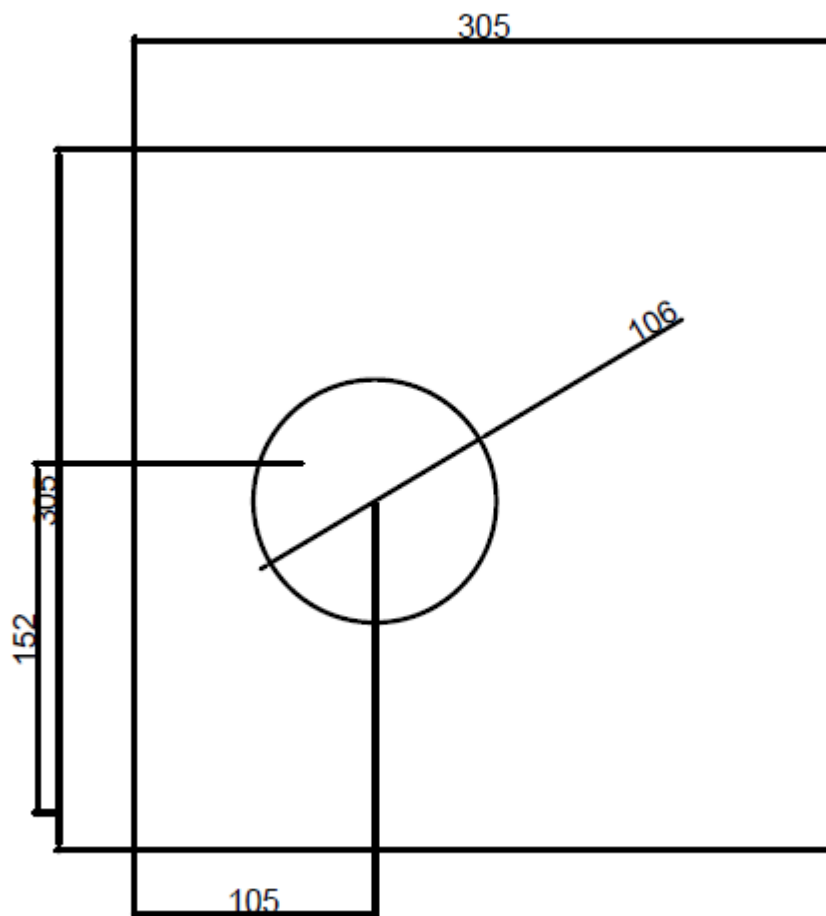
Dimensões do anteparo com furo, cotas em milímetros
